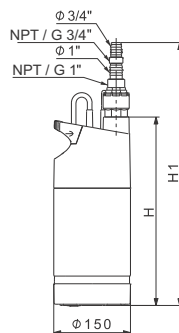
Bomba SB. as mesmas dimensões com filtro de aspiração integrado e com filtro de aspiração flutuante
